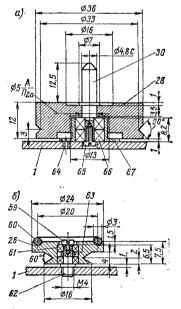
Узел ведущего вала (а) и промежуточного шкива (б): 1— панель лентопротяжного механизма (ЛІПМ); 26— шкив промежуточный, ЛС59-1; 28 — маховик, ЛС59-1; 30 — ведущий вал, Ст. XВГ, калить HRC58... 60, запрессовать в дет. 28; 59 — винт $M2 \times 2$; 60 — кольцо, резина, приклеить к дет. 26 клеем 88-н; 61 — подшинник шариковый 2000083 ($7 \times 3 \times 2.5$ мм), 2 шт.; 62 — стойка, Ст. 2×1.5 (3 — втулка, Д16-Т; 64 — винт $M2 \times 4$, 3 шт.; 65 — винт $M2 \times 5$; 66 — подшинник шариковый № 23 ($10 \times 3 \times 4$ мм), 2 шт.; 67 — втулка, ЛС59-1. Рис. 3. Узел ведущего вала (а) и про-
